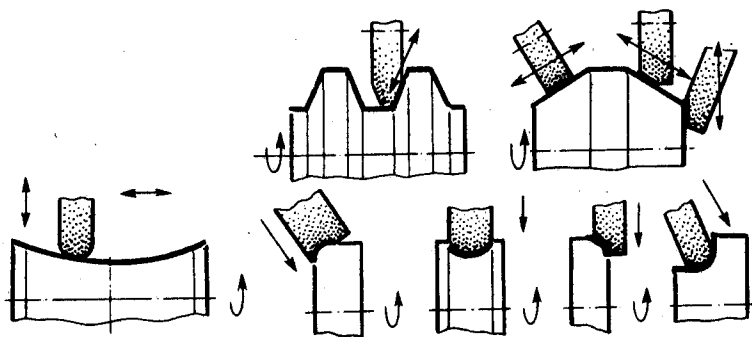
Примеры профильного шлифования рабочих рунцов валков прокатных станков
